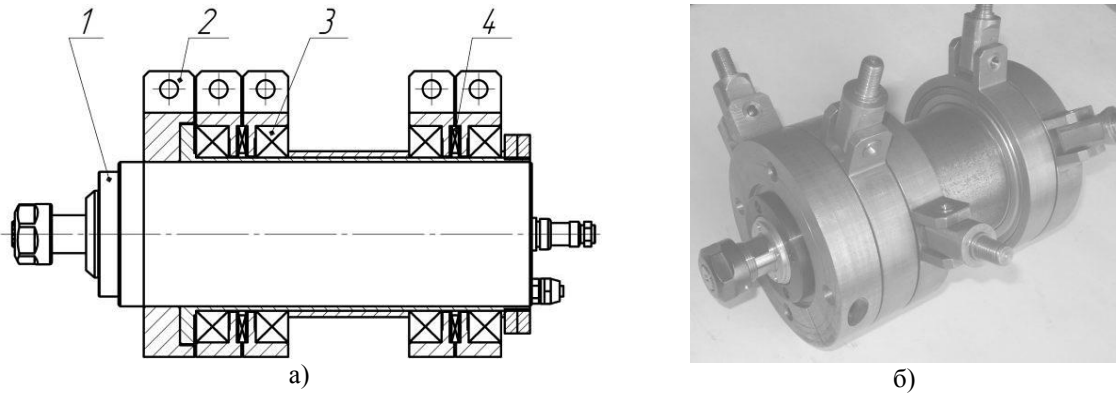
Робочий орган батокординатного верстата «пентапод»: а) конструкція, б) загальний вигляд
